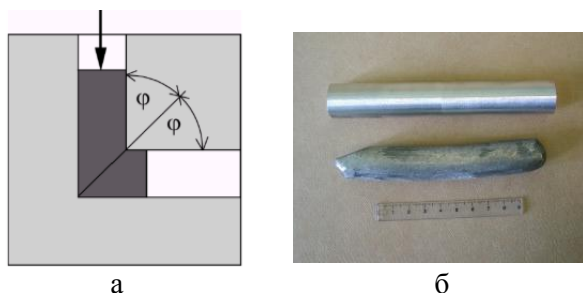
Схема равноканального углового прессования (а) и внешний вид прутковых заготовок до и после РКУП (б).
